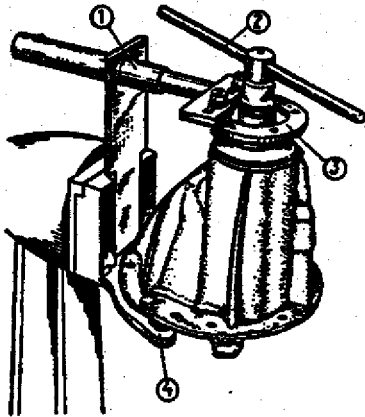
Remoção da porca do flange do pinhão: 1 - dispositivo para fixar o flange do pinhão; 2 - chave com soquete; 3 - flange do pinhão; 4 - suporte.
